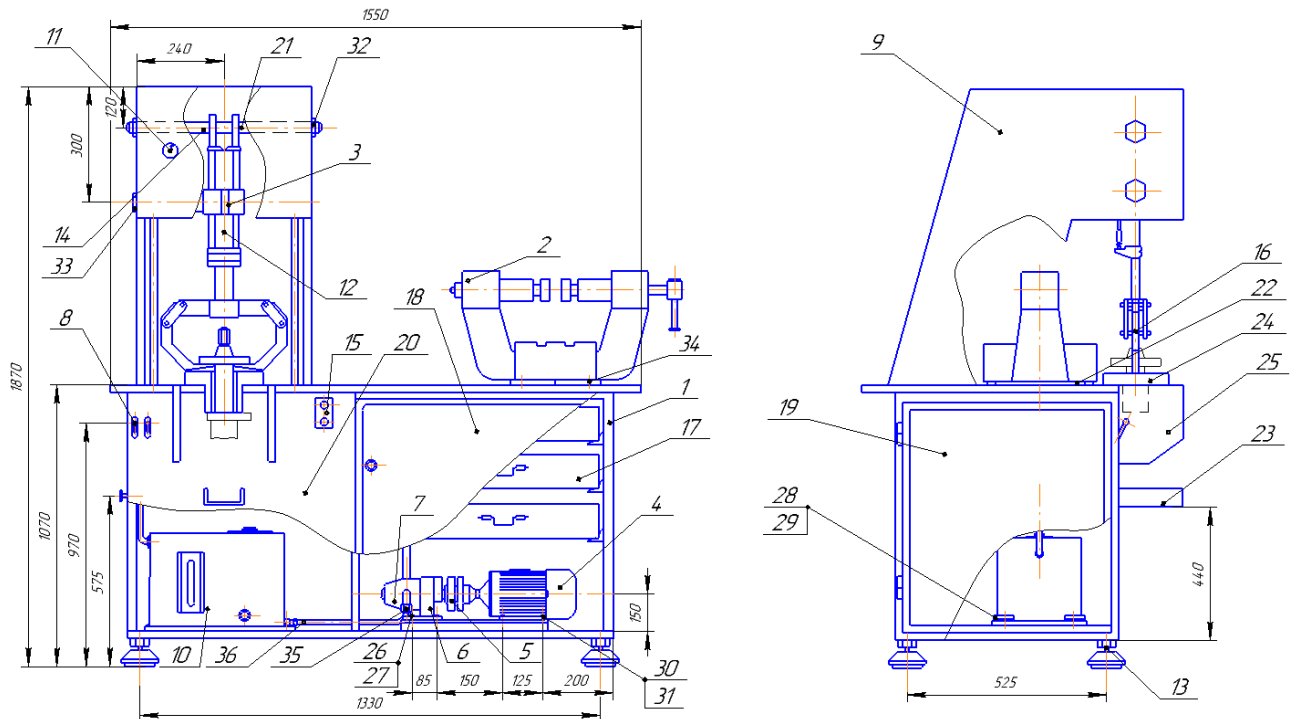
Загальний вид конструкції станда: 1 – Рама; 2 – Струбцина; 3 – Опора фіксуюча; 4 – Електродвигун; 5 – Муфта; 6 – Пристрій для кріплення; 7 – Гідравлічний насос; 8 – Гідророзподільник; 9 – Укосина; 10 – Бак гідравлічний; 11 – Манометр; 12 – Гідроциліндр; 13 – Опора; 14 – Панель кронштейна; 15 – Кнопочка станція; 16 – Знімач; 17 – Ящик; 18 – Двері передні; 19 – Двері бічні; 20 – Панель ліва; 21 – Вісь; 22 – Плита опорна; 23 – Уловлювач; 24 – Втулка упорна; 25 – Ребро; 26-34 – Різьбові з’єднання; 35 – З’єднання роз’ємні рукавів; 36 – Рукав
